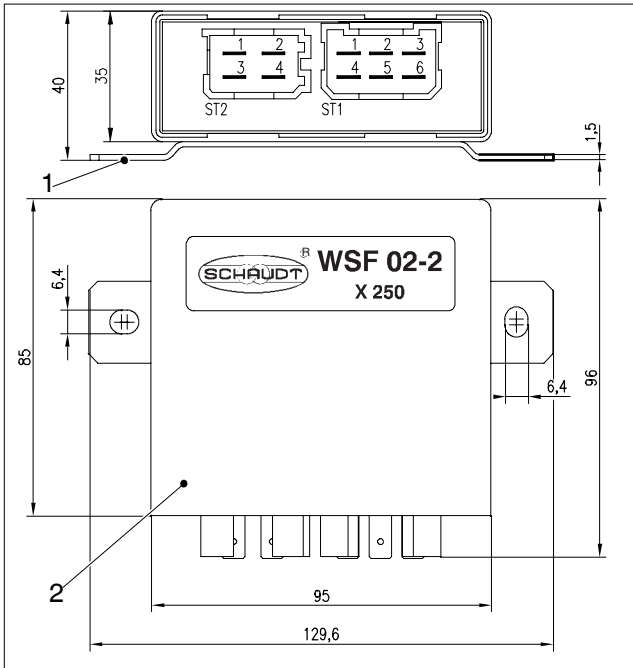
Maßbild Motorsteuerung WSF 02-2 (Abmessungen in mm)
